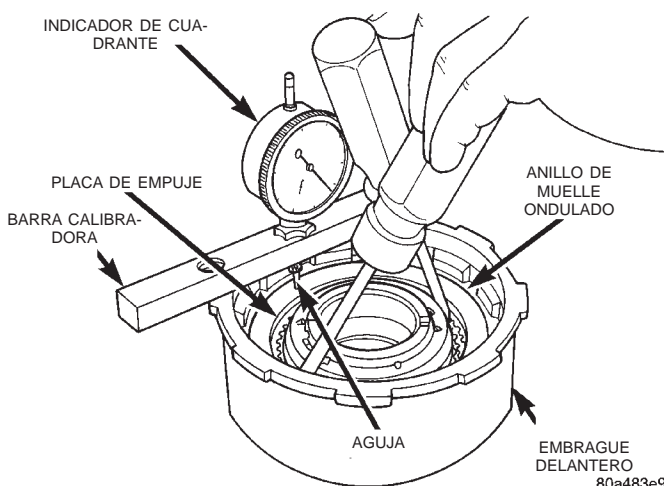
Medición de la holgura del conjunto del embrague delantero
